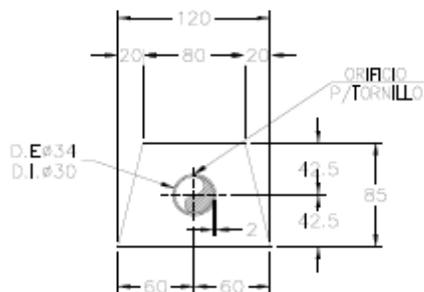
Corte D-D. Detalle geométrico de rebaje para tornillo, equipado con arandela plana.
